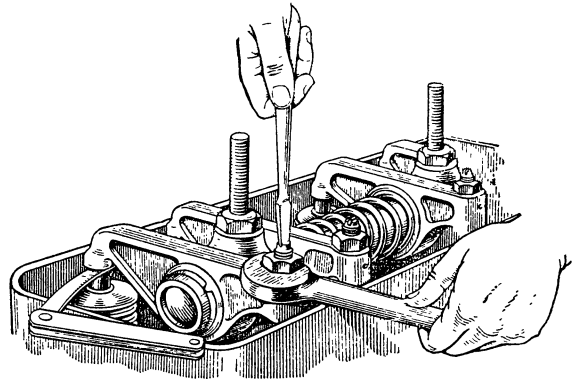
Регулировка зазора между клапаном и бойком коромысла.
